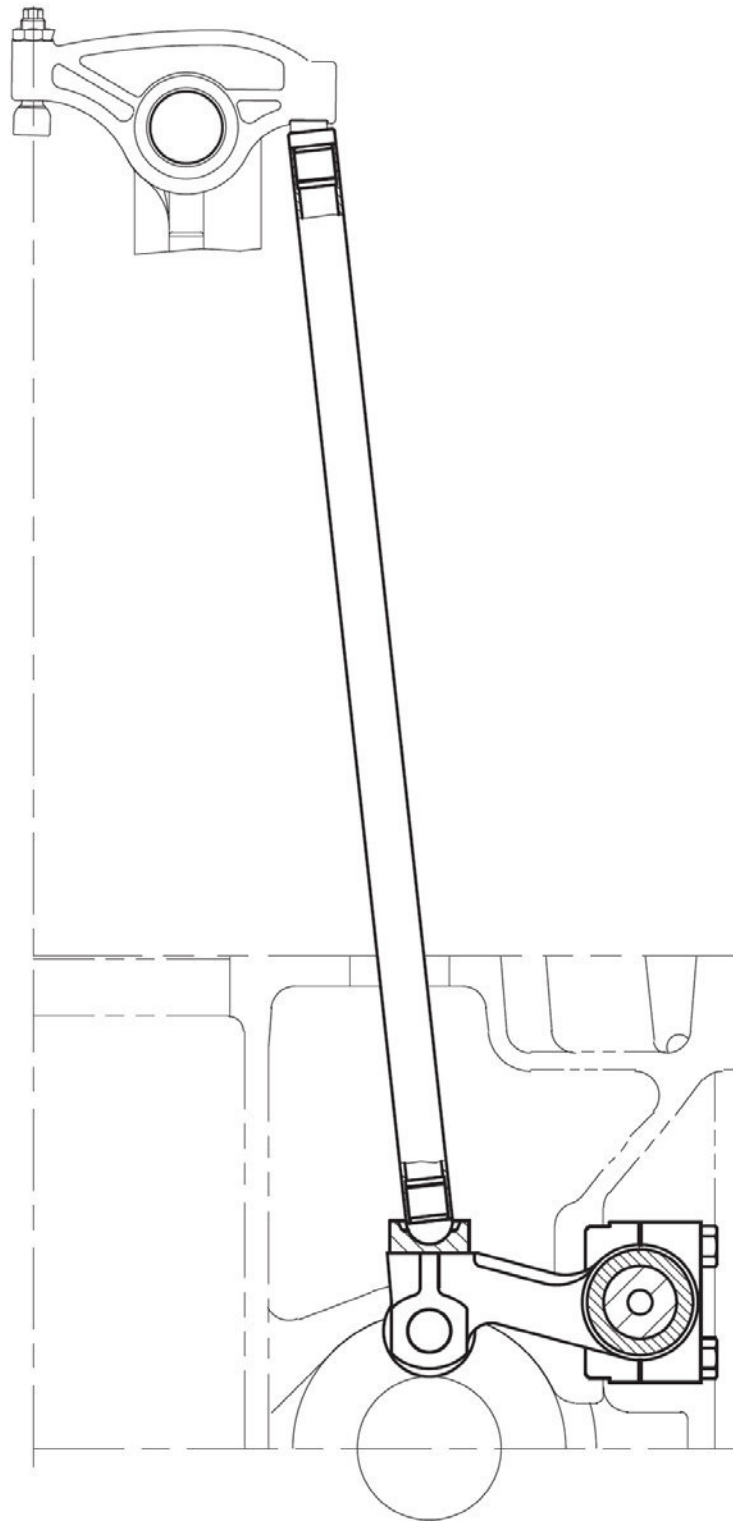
Штанга штовхача дизеля МаК 32С
